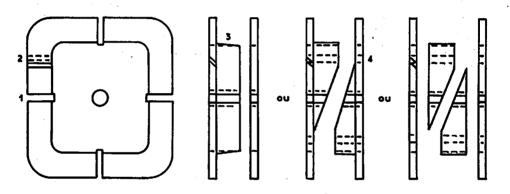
Gabarit pour bobinage d'un inducteur.
